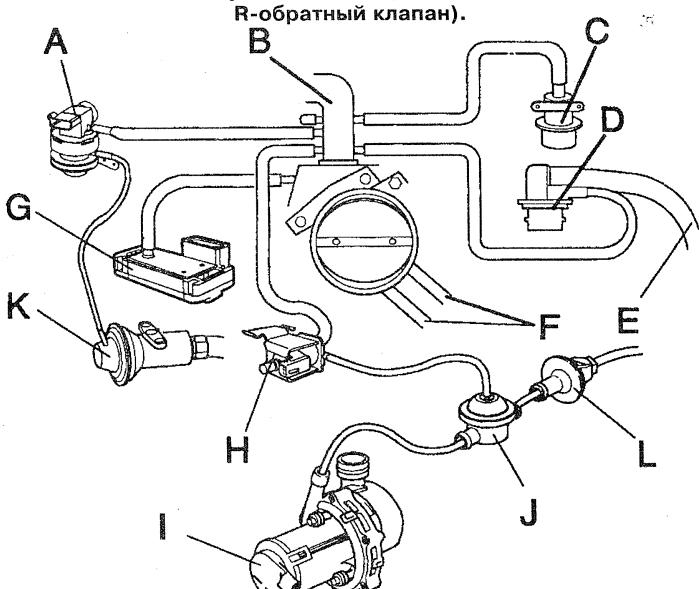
б (A-преобразователь EG, B-соединения, C-регулятор давления, D-блок управления вентиляцией картера, Е-шланг маслоулавливателя, F-шланги системы EVAP, G-датчик давления, H-магнитный клапан, I-воздушный насос, J-запорный клапан, K-клапан EGR, L-обратный клапан).
